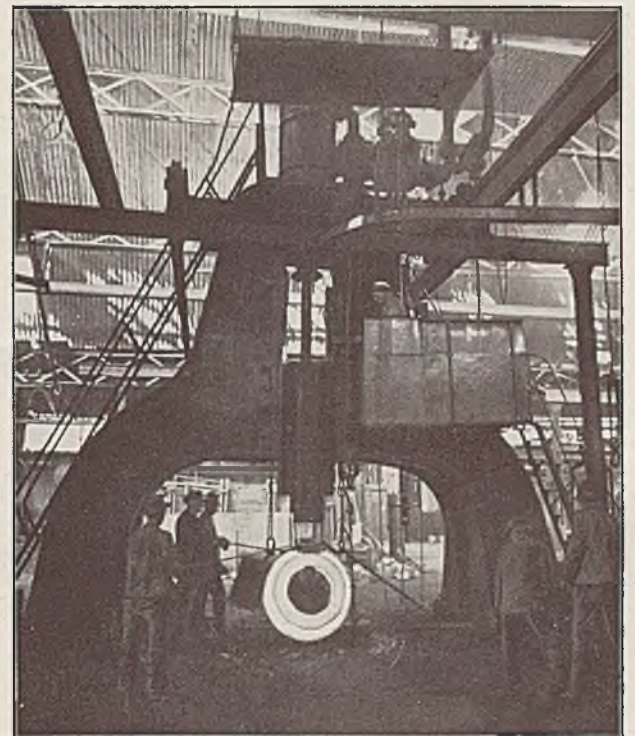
Hornhammer mit einem Bargewicht von 3,5 t
